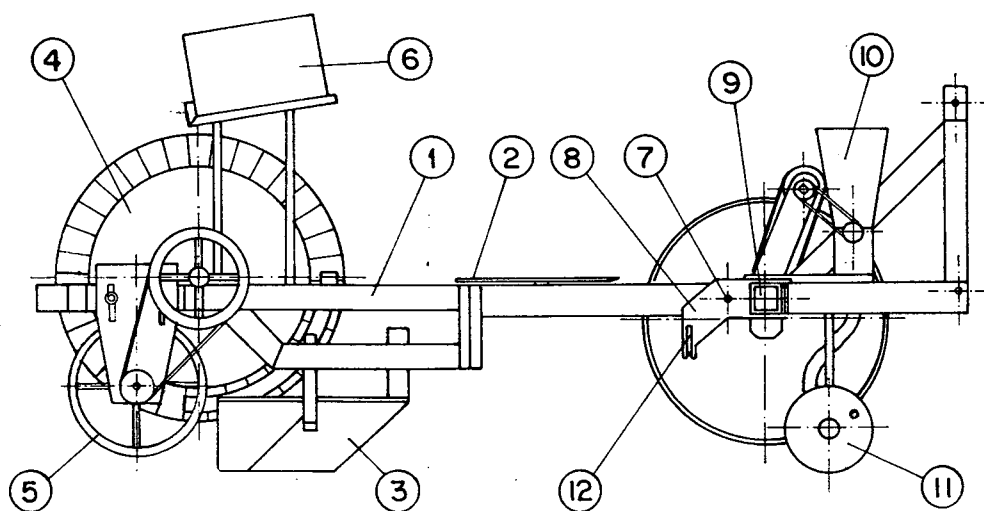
Vista lateral do módulo de plantio acoplado à carreta.
